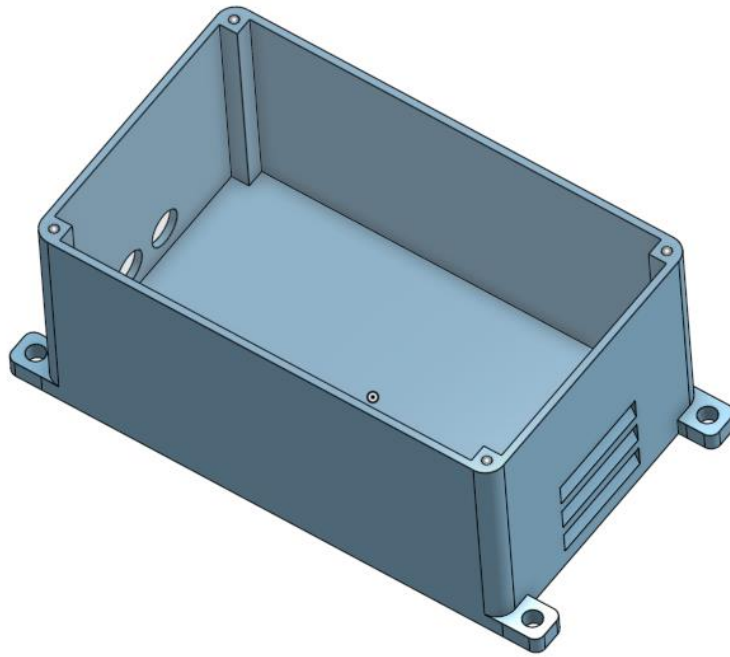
3D-модель основної частини корпусу внутрішнього блоку
